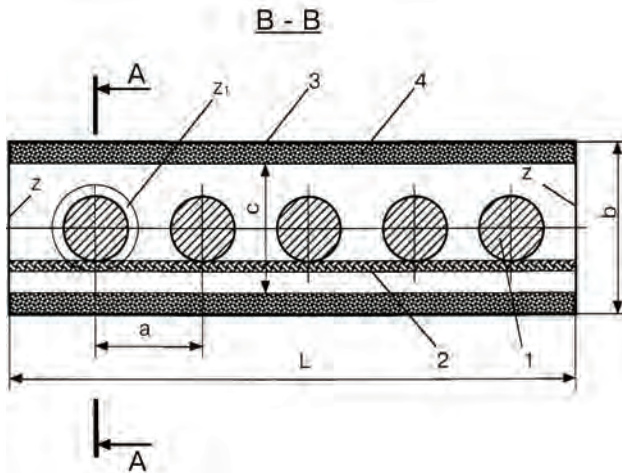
б. Поперечный разрез звукоизолирующего кожуха для машины типа «VTS-07»: 1–веретено, 2–тангенциальный ремень привода веретен, 3–металлические стенки кожуха, 4–звукопоглощающий материал.
